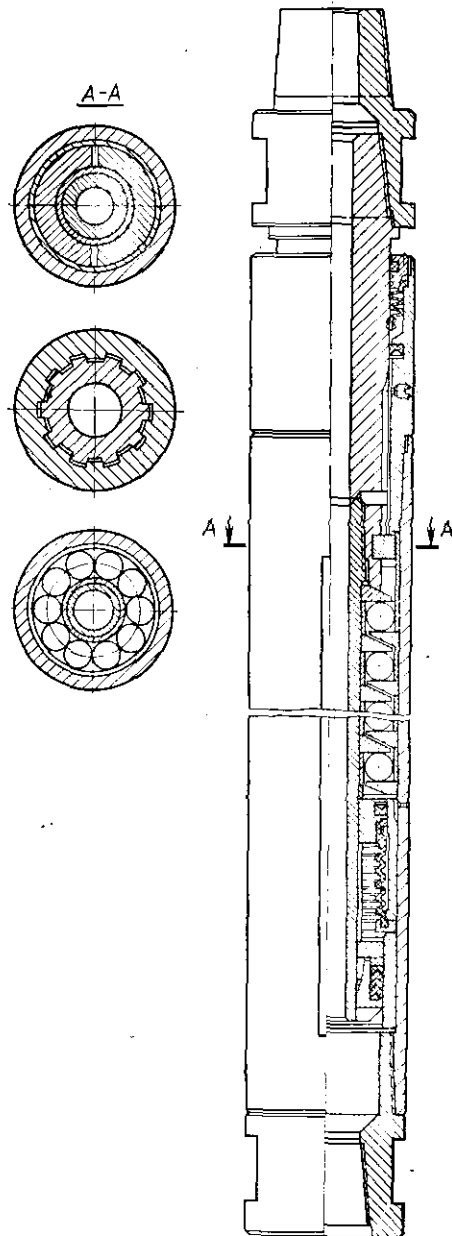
Схема забойного амортизатора для шарошечного бурения
